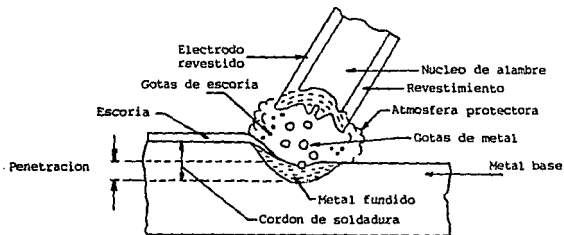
Esquema del proceso de soldadura por arco eléctrico con electrodo revestido.
